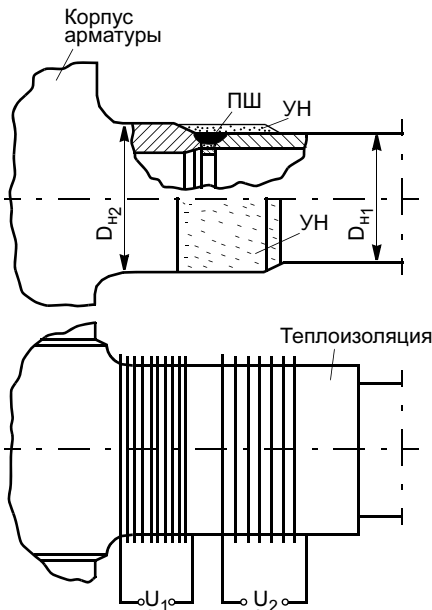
Рекомендуемая схема сварочной технологии ремонта стыкового сварного соединения разнотолщинных трубных элементов  $\varnothing 290 \times 50$  мм/ $\varnothing 273 \times 32$  мм (сталь соответственно 15X1M1ФЛ/12X1MФ, металл шва 09X1MФ): а, б — см. рис. 7
